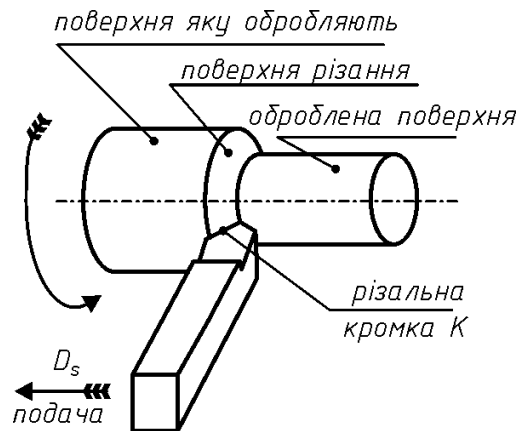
Поверхні заготовки та різця: К – різальна кромка,  $D_s$  – напрям подачі
